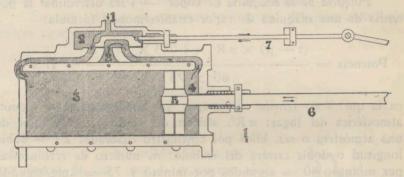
Corte esquemático de distribución de una máquina a vapor.
